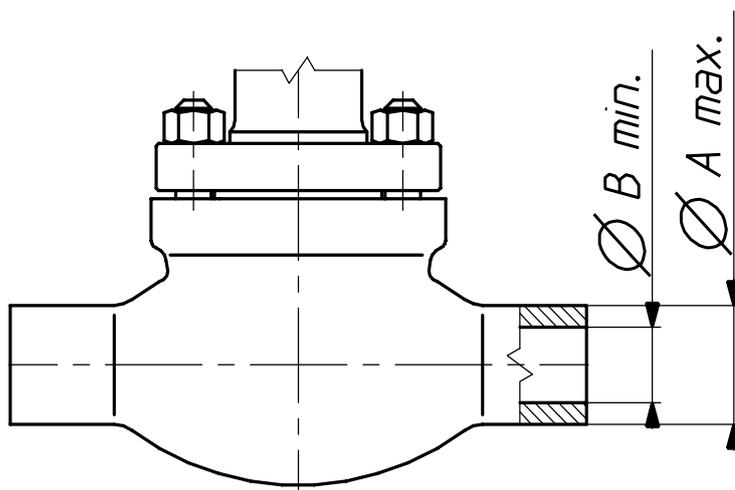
Размеры выводов для сварки, изготовленных из отливки.
